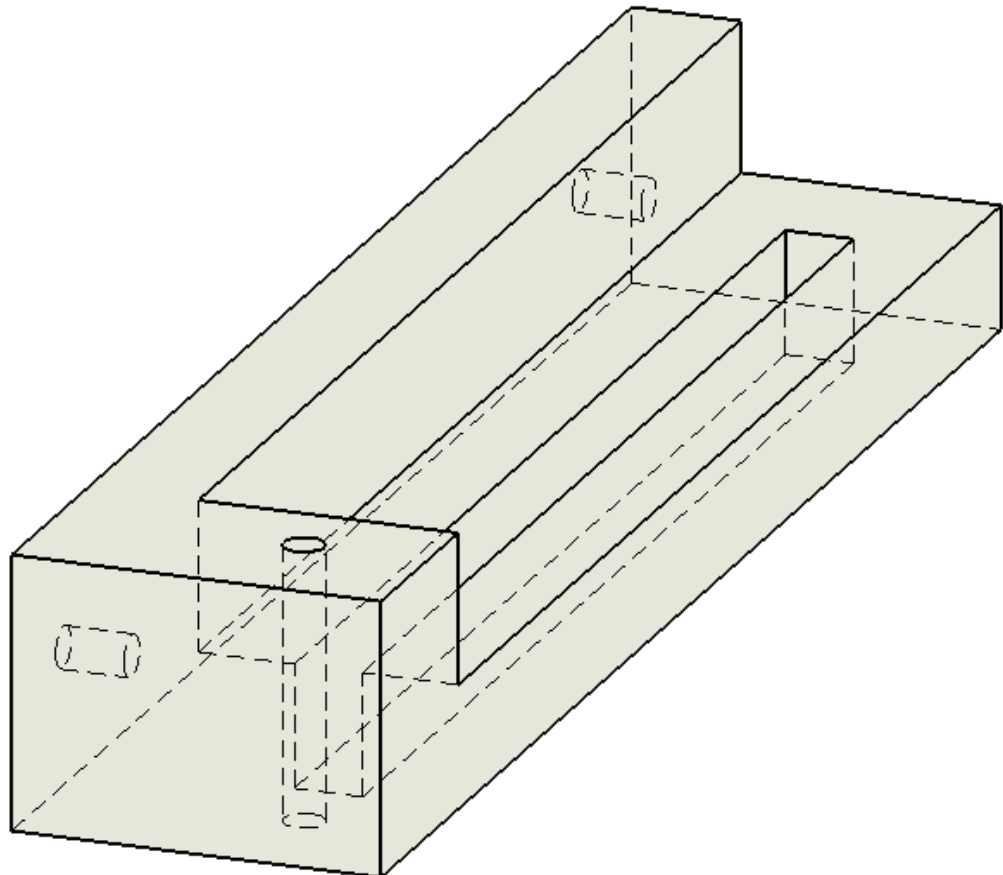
Outline de peça modelada (Suporte) – Fonte: Elaboração própria
